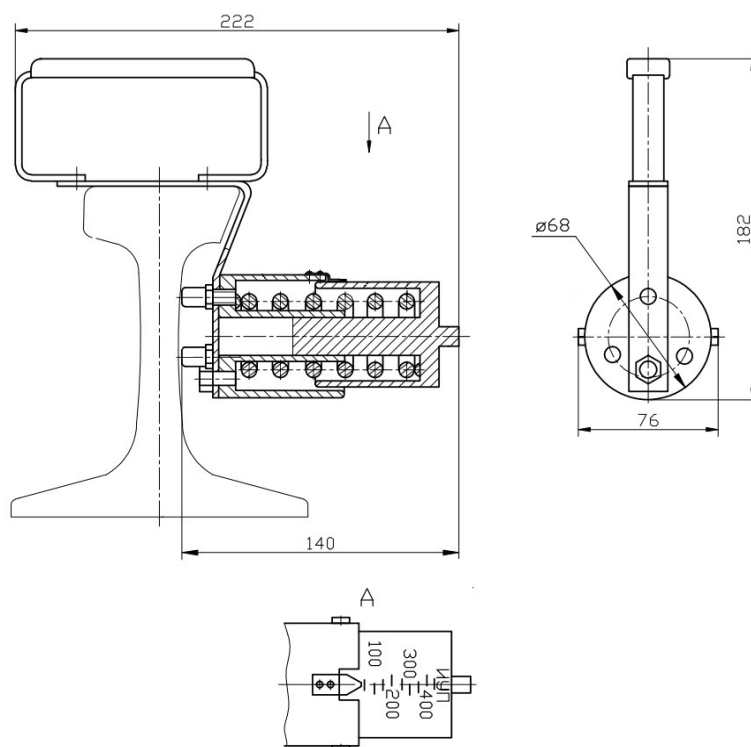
Внешний вид и габаритные размеры индикатора
